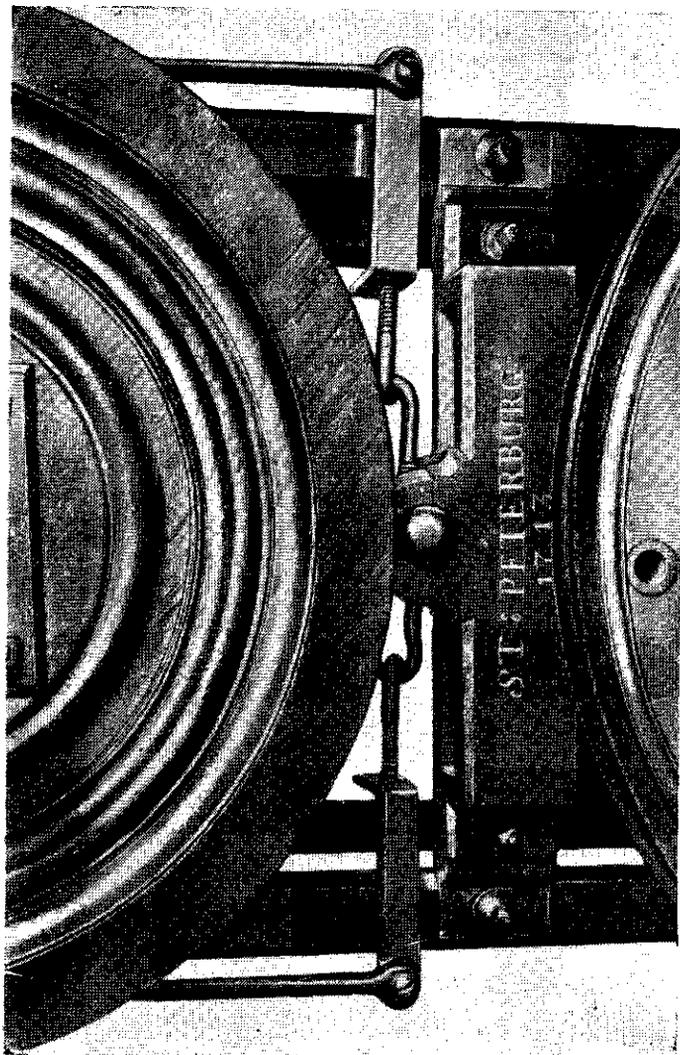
Узел привода и подвески патрона-главной токарно-гильоширного станка Нартова 1713 г.
